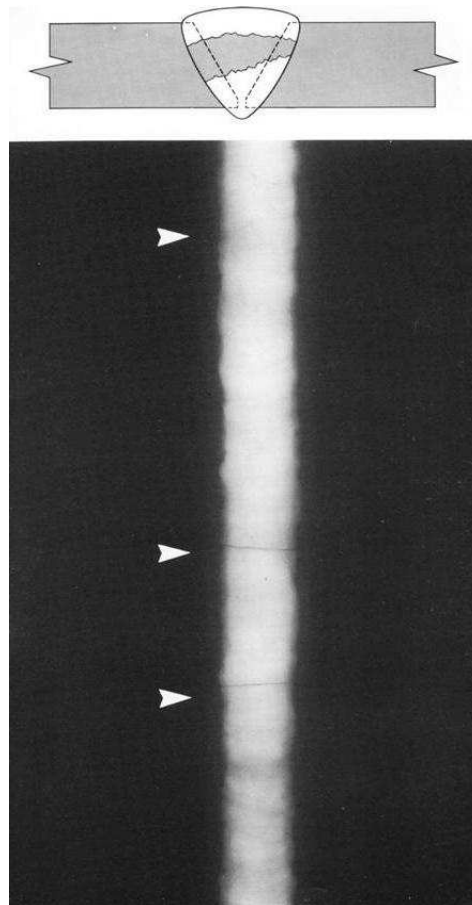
23 *Fisuras transversales en la junta soldada.
